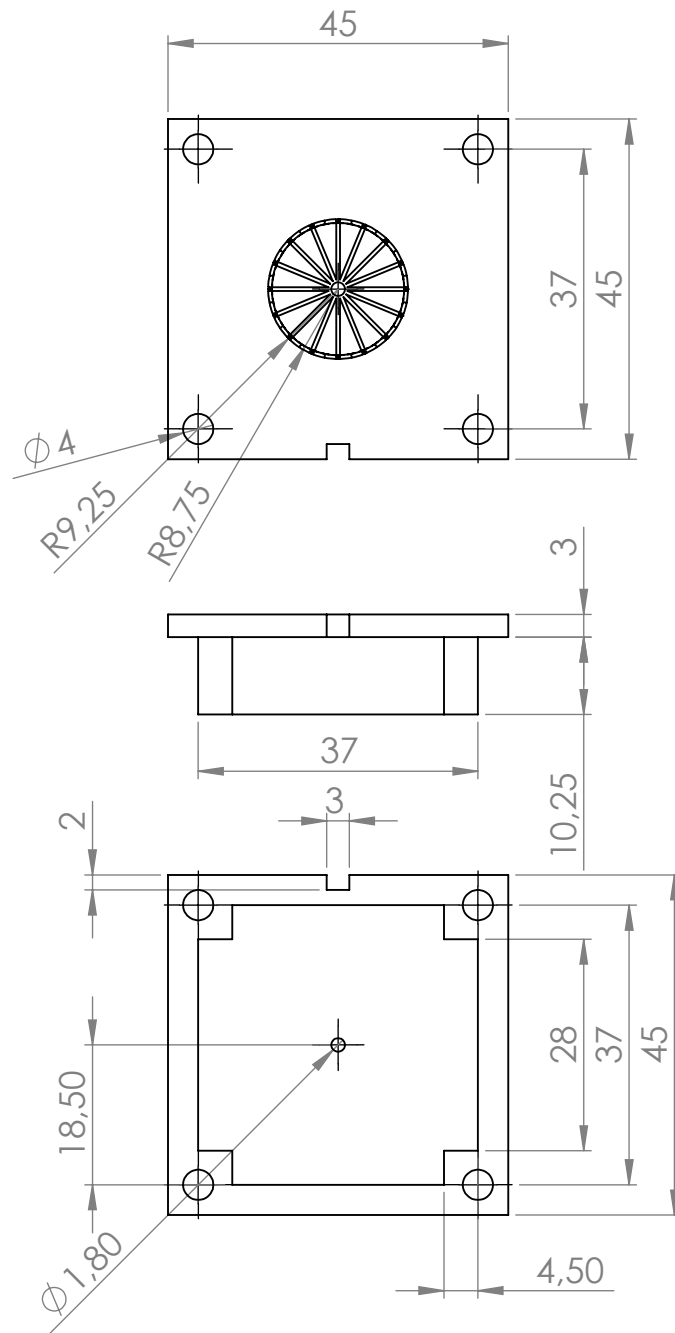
Diseño del molde para enmallado interno del *Robot Biaxial* parte A
